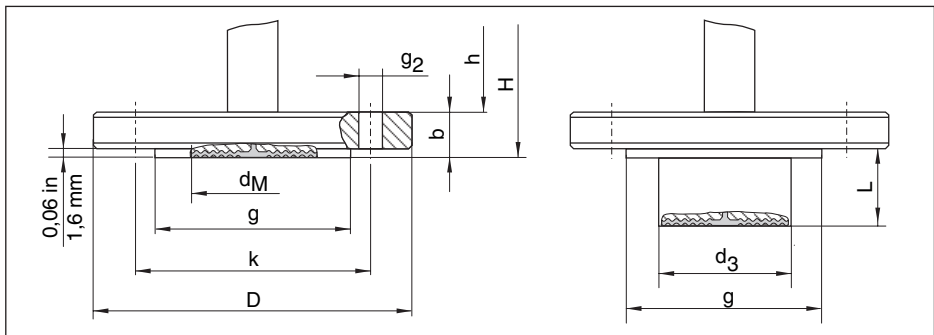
Prozessanschluss VEGADIF 65 mit Druckmittler einseitig, Plusseite EN-/DIN-Flansch mit und ohne Tubus, 316L
